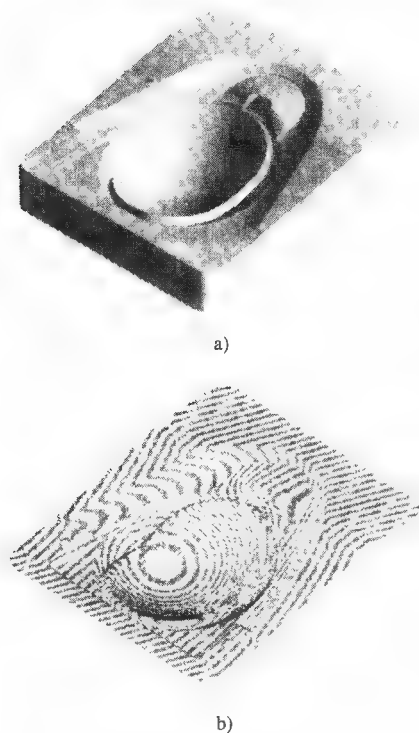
修改前的阶梯模板及其生成的刀具路径
